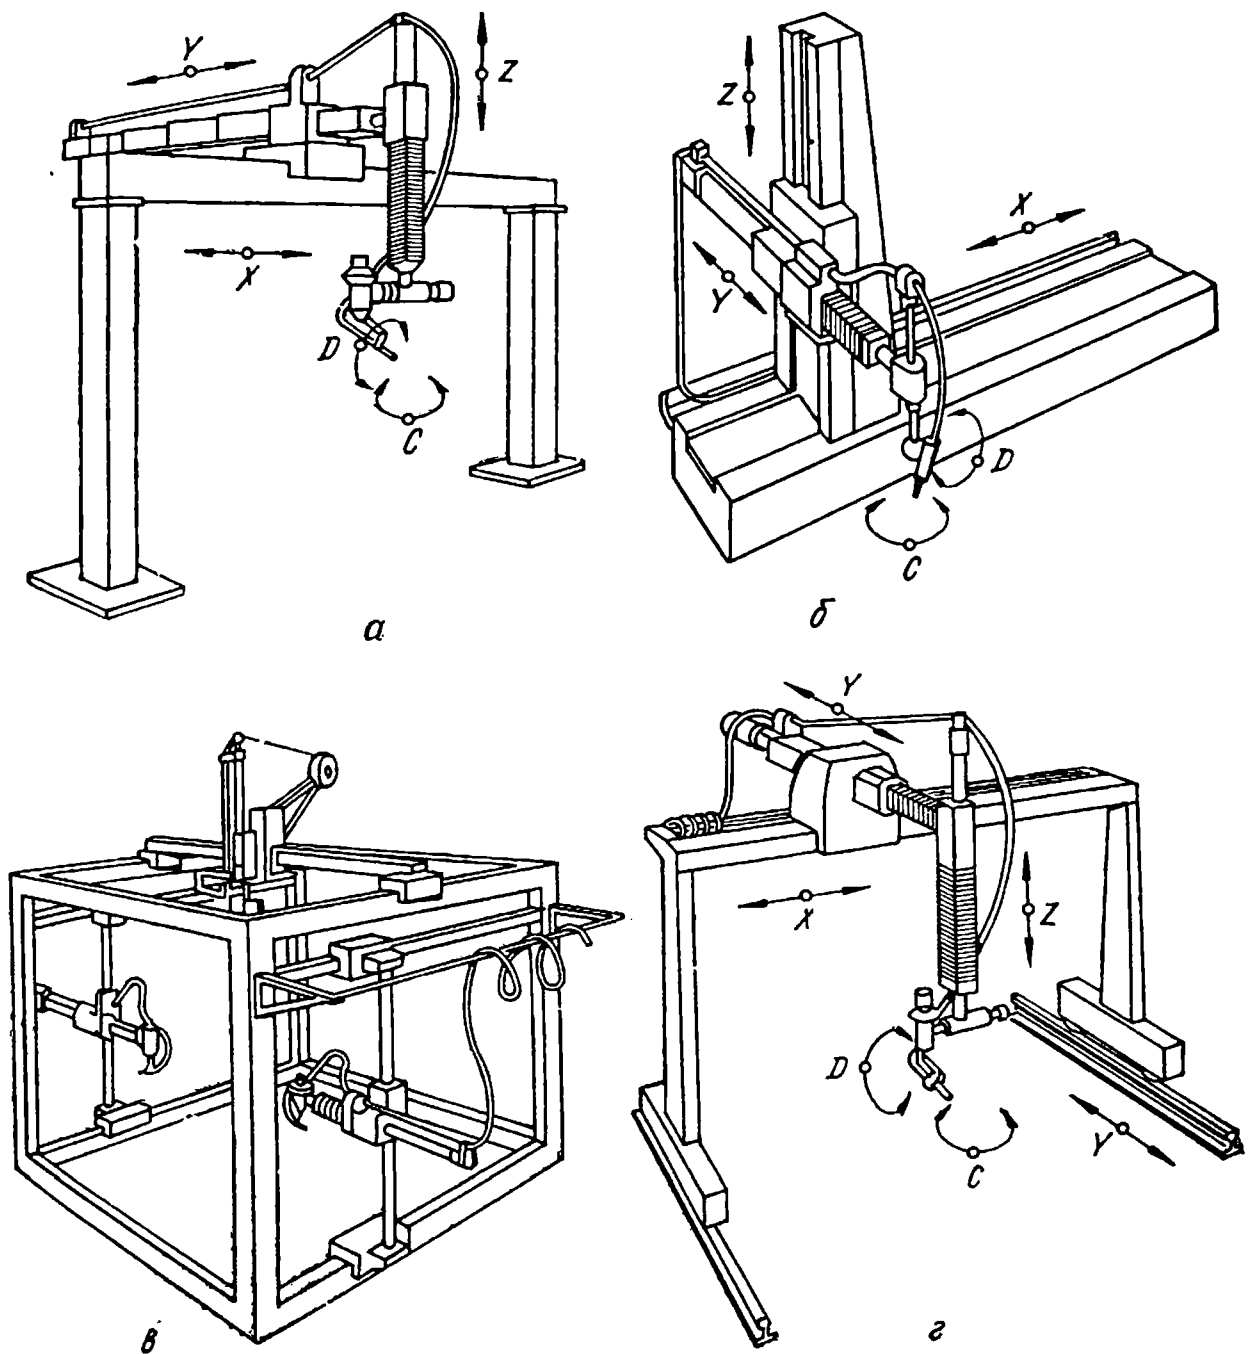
Компоночные схемы манипуляторов сварочного инструмента с прямоугольной системой координат переносных движений:
